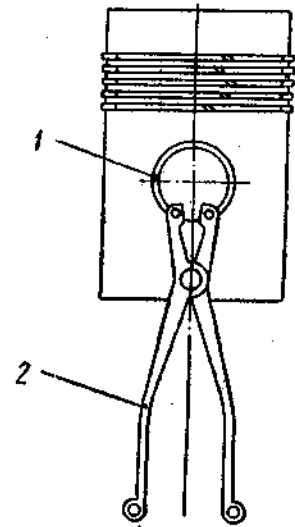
Съем и установка стопорного кольца поршневого пальца:
